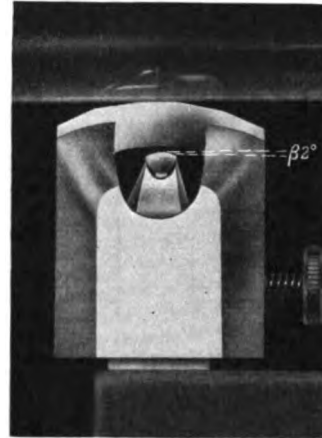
Der Diamant steht auf Schnitt, sobald eine der Visierfaceretten am Werkstück zum Anliegen gebracht wird.
